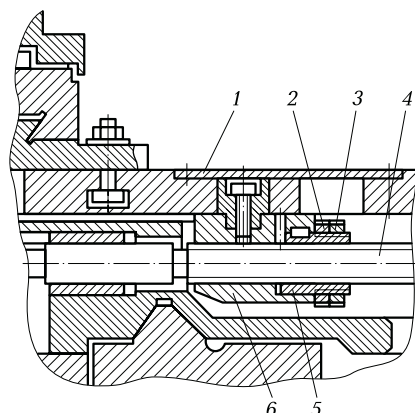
Регулирование зазора между ходовым винтом и гайкой механизма поперечной подачи токарного станка:
